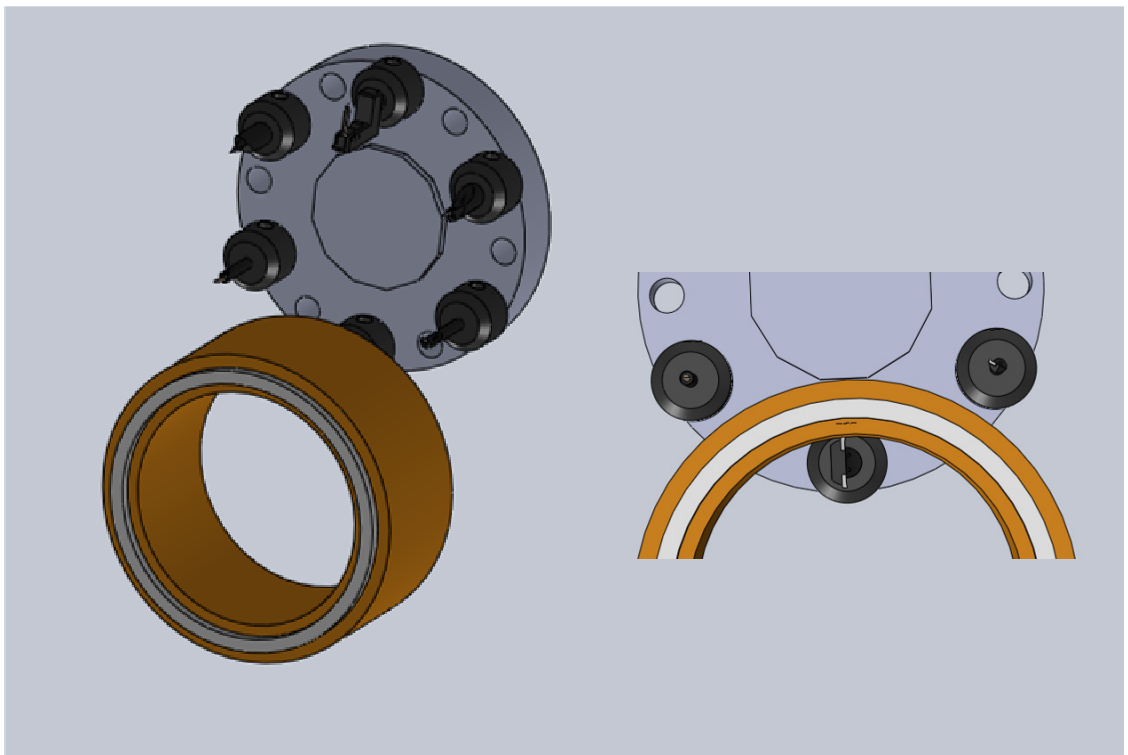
12-fach Werkzeugwender Durchmesser 300mm mit Halbzeug 265/350
